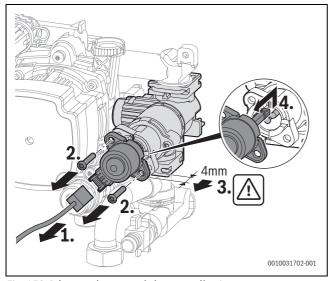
Démonter le moteur de la vanne sélective Monter le moteur.
